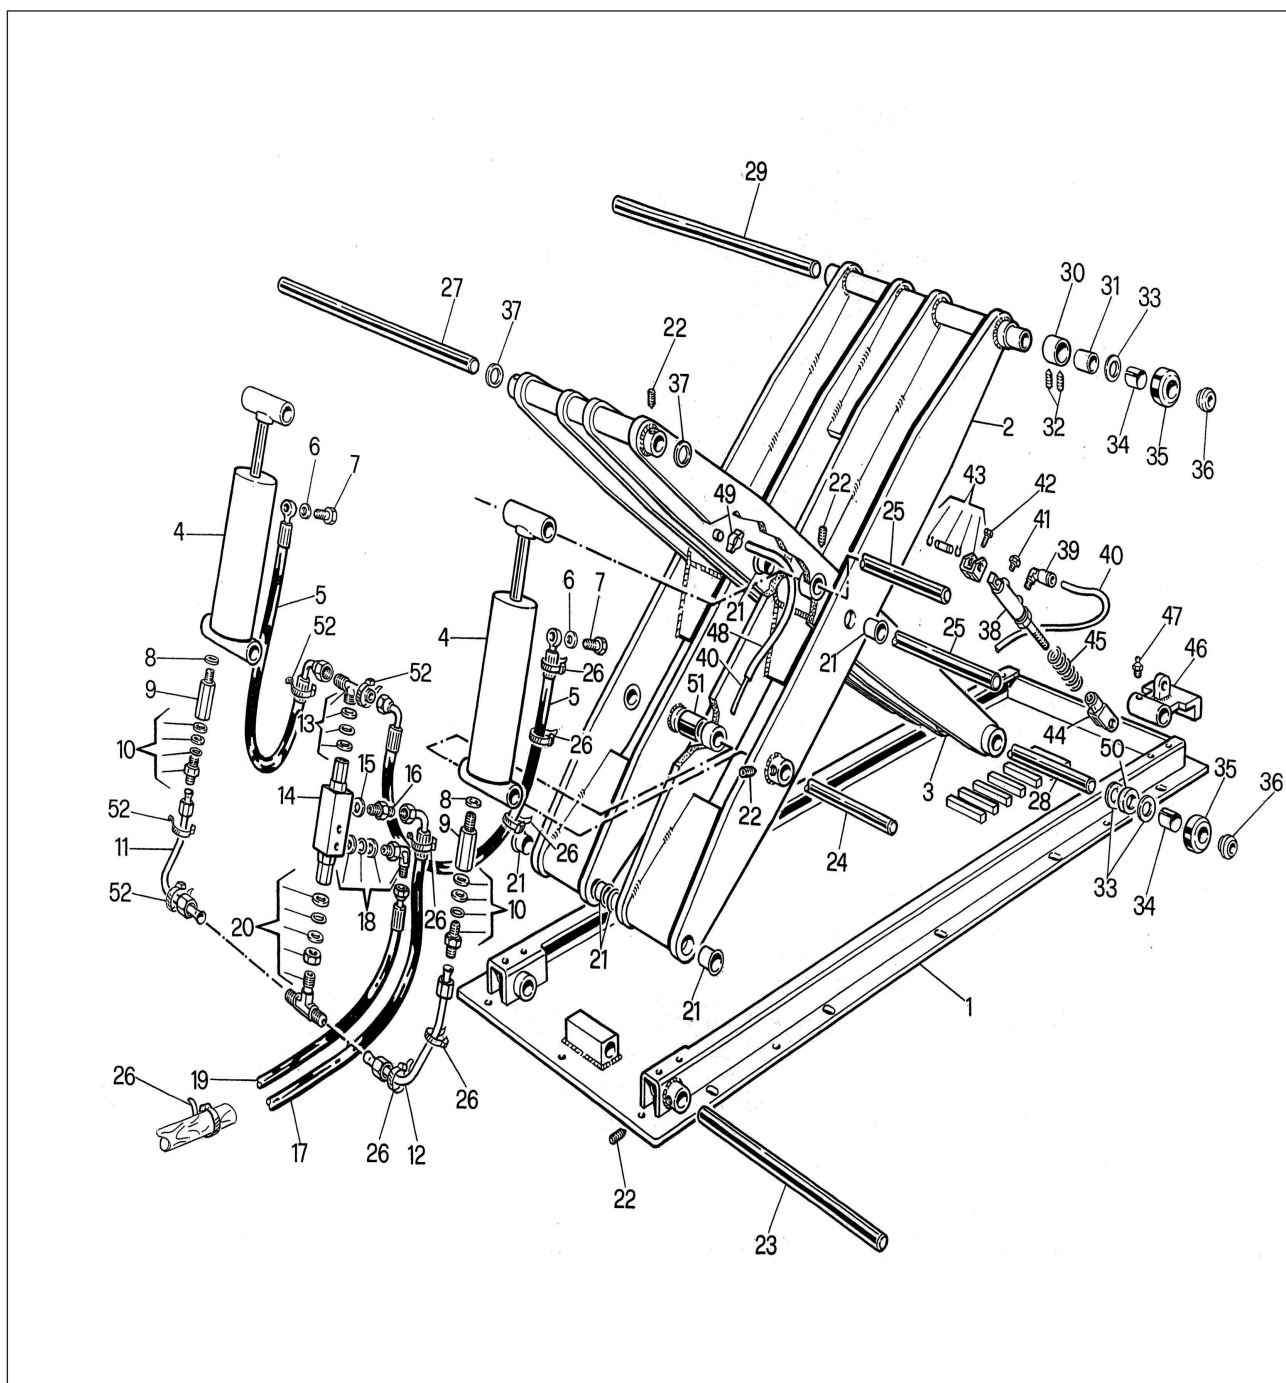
ESTRUCTURA DEL ELEVADOR
